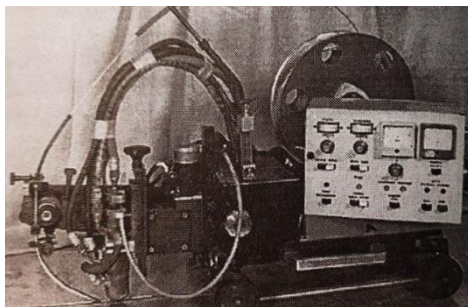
Автомат для плазменно – дуговой сварки УПДС
